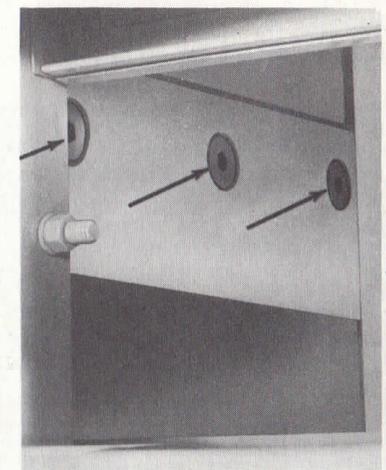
Accessibilité et démontage du couteau de presseur.
